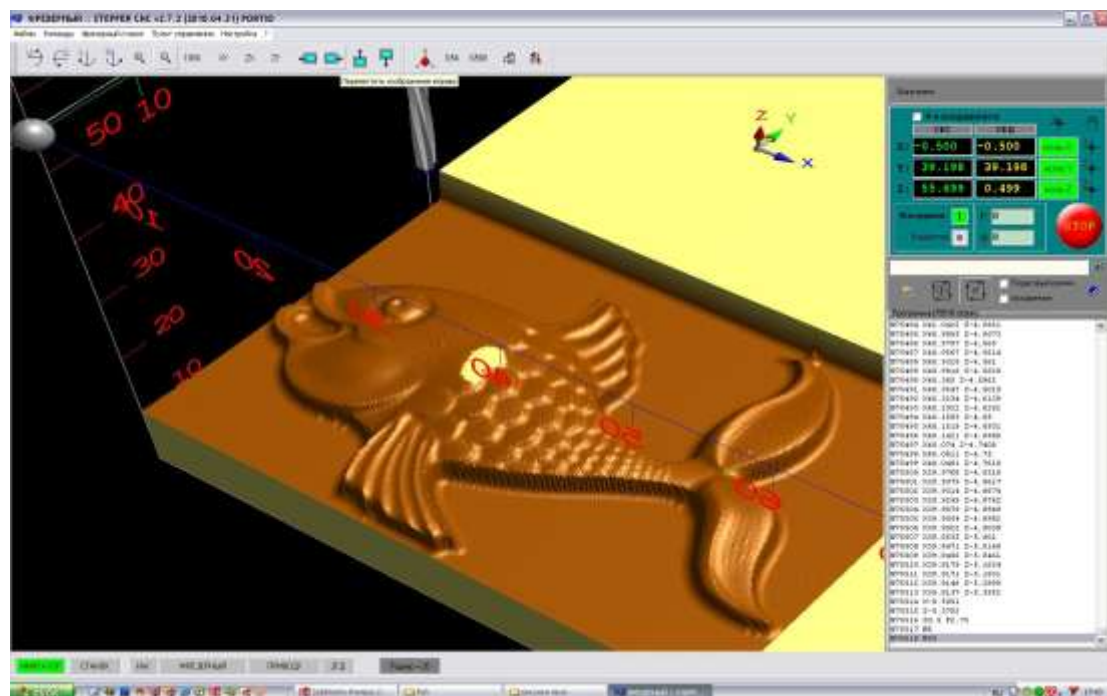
Изготовление виртуальной детали в имитаторе фрезерного станка с ЧПУ по программе сгенерированной в ADEM
